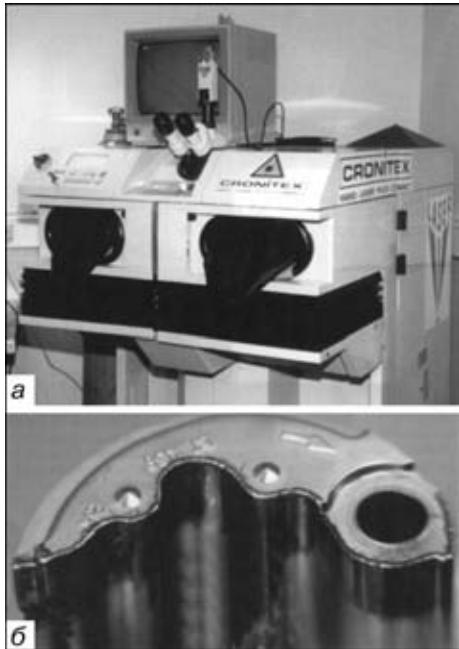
Установка для ручной лазерной обработки и наплавки (а) и внешний вид наплавленной детали (б)
